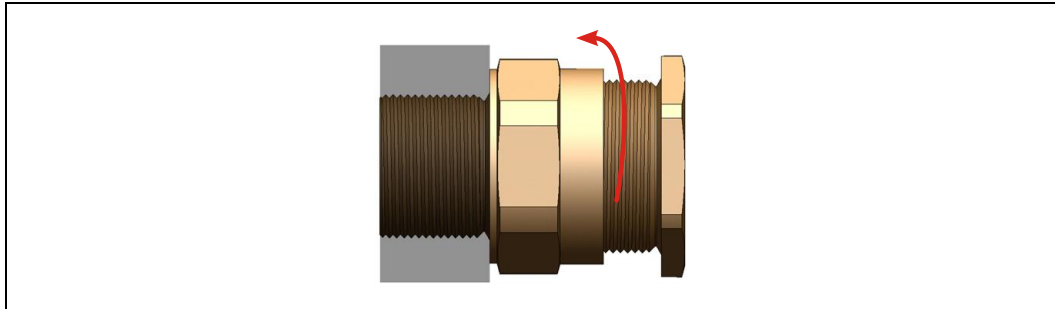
Einschrauben der Kabeleinführung in die Anschluss-Haube
